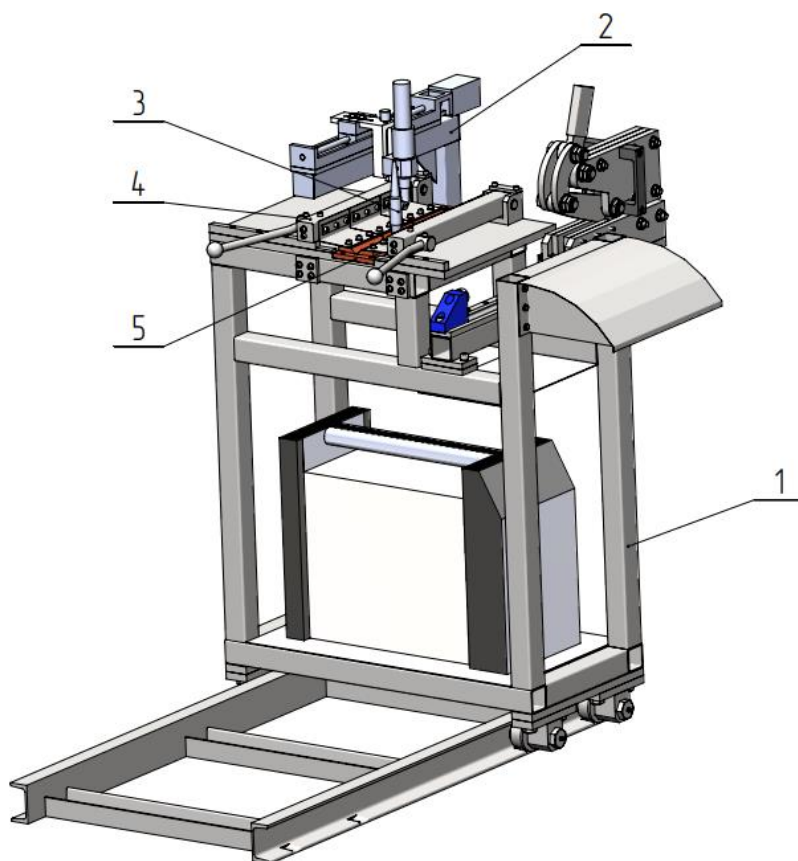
Общий вид сварочного узла ЛА100-04.11.00.000М
